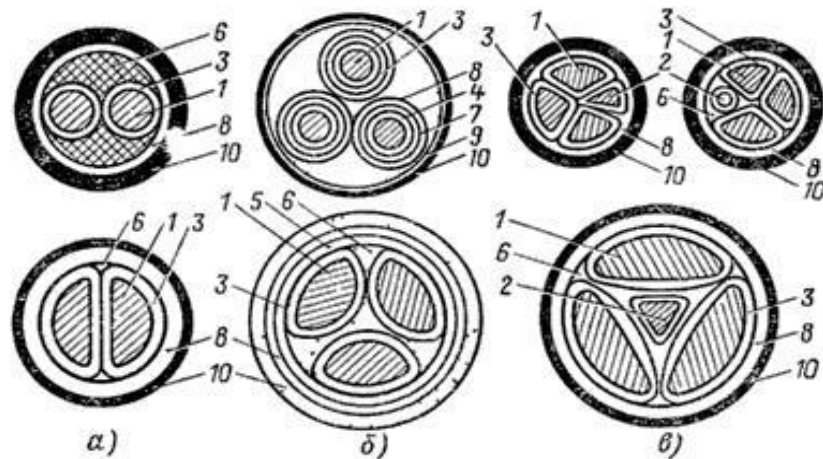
Переріз силових кабелів: а – двожильні кабелі з круглими і сегментними жилами, б – трижильні кабелі з поясною ізоляцією і окремими оболонками, в – чотирьохжильні кабелі з нульовою жилою круглої, секторної і трикутної форми, 1 – струмопровідна жила, 2 – нульова жила, 3 – ізоляція жили, 4 – екран на струмопровідній жилі, 5 – поясна ізоляція, 6 – заповнювач, 7 – екран на ізоляції жили, 8 – оболонка, 9 – бронепокрив, 10 – зовнішній захисний покрив.
